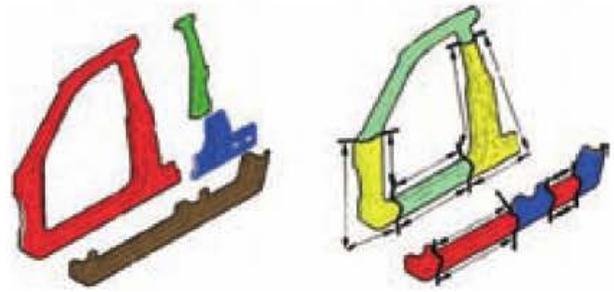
Despiece y líneas de corte establecidas por el fabricante para el Ford Focus.
